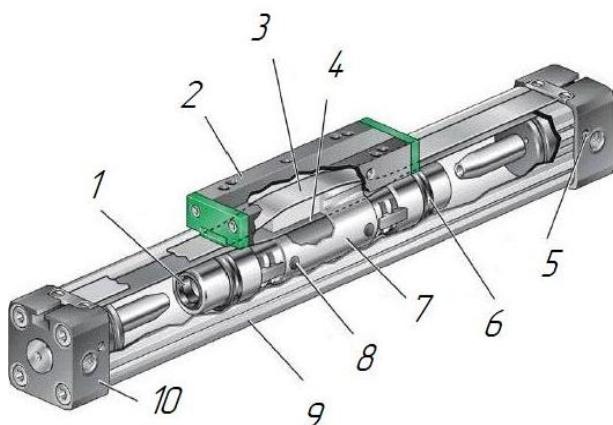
Цилиндр пневматический бесштоковый 1605
